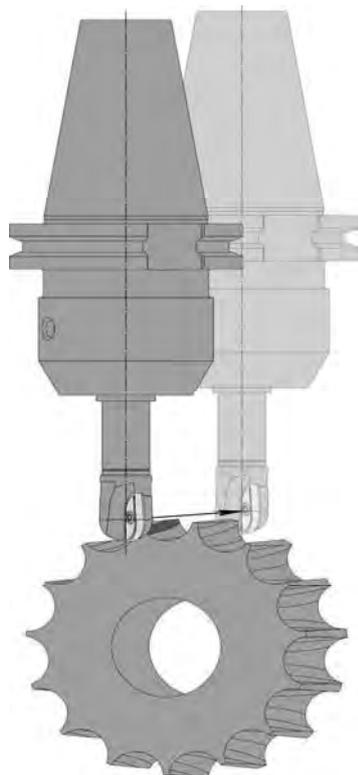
Схема формообразования участка поверхности зуба сателлита сферической фрезой на станке с ЧПУ
